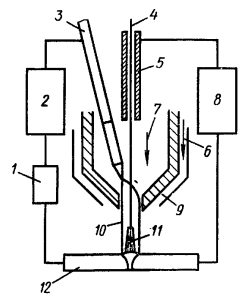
Схема комбинированного способа — плазменно-дуговой сварки плавящимся электродом:
